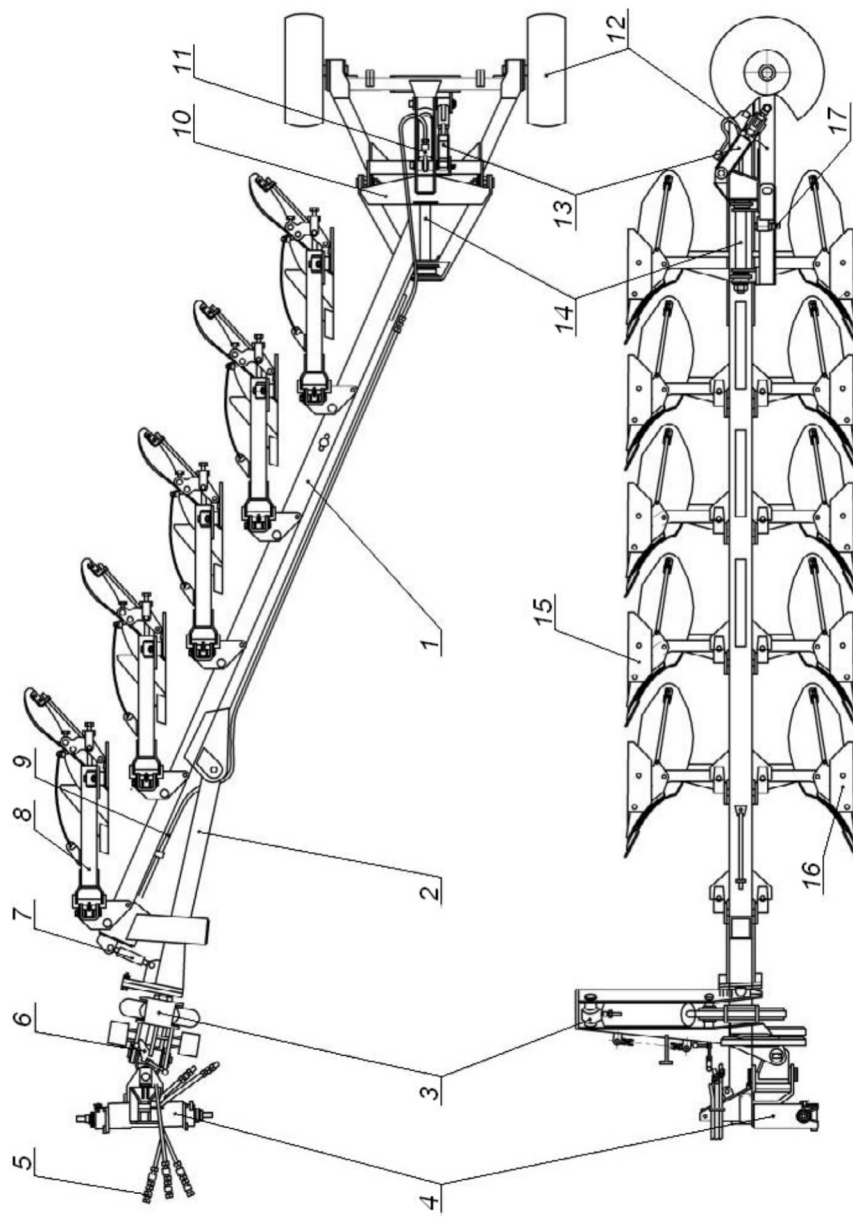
Плуг пятикорпусный полунавесной оборотный ПШО-5-40: 1 – рама; 2 – балка тяговая; 3 – механизм оборота рамы; 4 – навеска; 5 – гидросистема; 6 – фиксатор; 7 – тагрел; 8 – предохранитель; 9 – трубопровод; 10 – рама; 11 – гидроцилиндр; 12 – ход колесный; 13 – механизм регулировки глубины вспашки задними корпусами; 14 – ось; 15 – корпус левооборачивающий; 16 – корпус правооборачивающий; 17 – болт регулировочный
